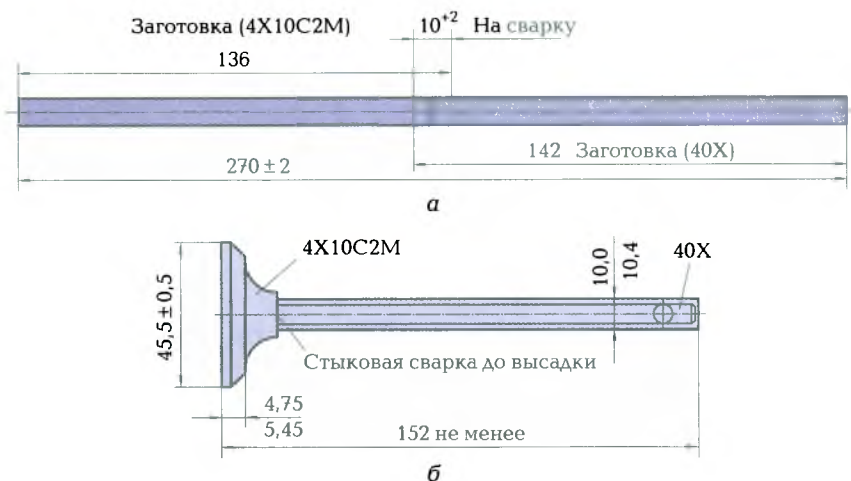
Заготовка клапана (а) и готовый клапан (б) из двух различных материалов, сваренных стыковой сваркой
